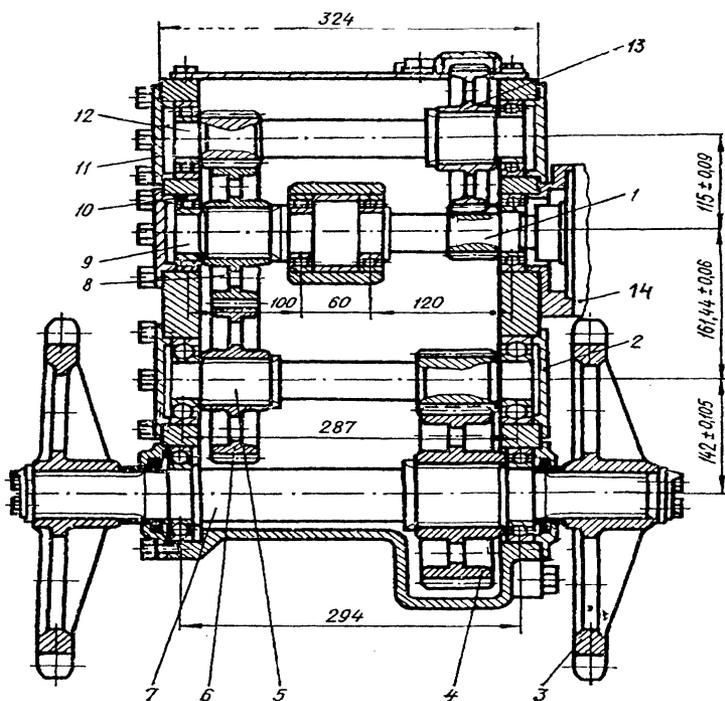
Редуктор привода ковшовой цепи каналоочистителя:
